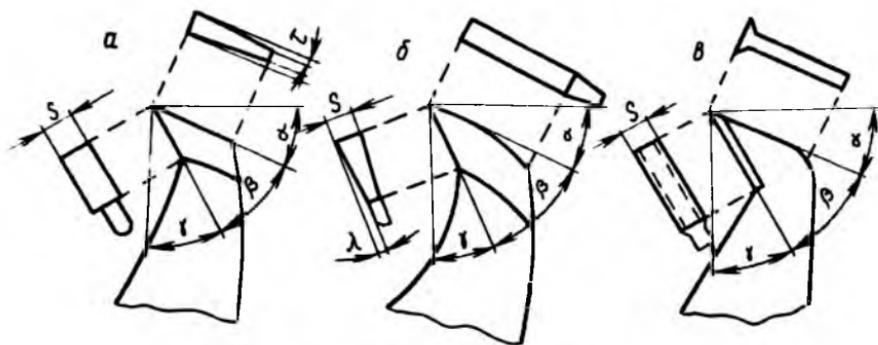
Режущие элементы двузубых фрез (крючьев)
